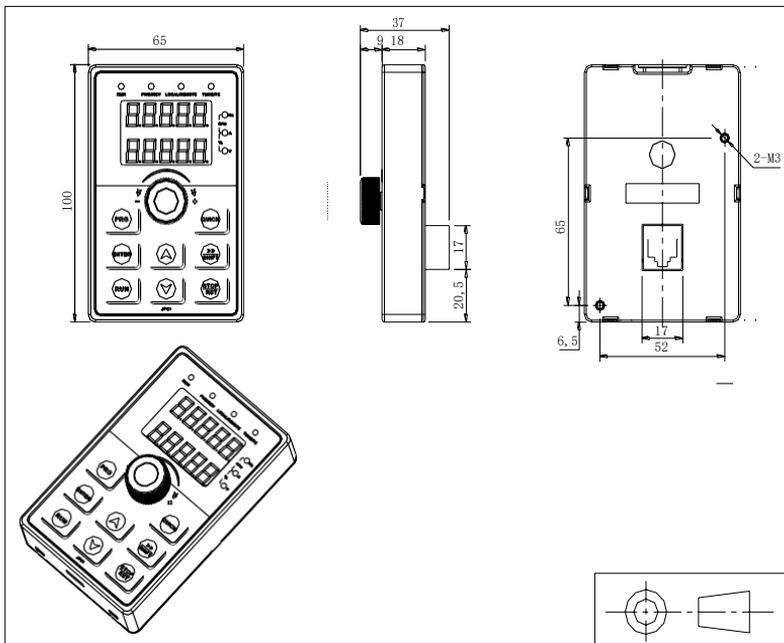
PI500-S Dimensional do teclado IHM (tamanho: mm)
